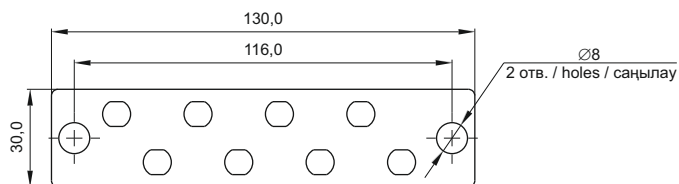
Габаритные и установочные размеры панели FOBX-P08-FC-R / Figure 5 – Overall and mounting dimensions of the panel FOBX-P08-FC-R / 5 сурет – FOBX-P08-FC-R панелінің габариттік және орнату өлшемдері
